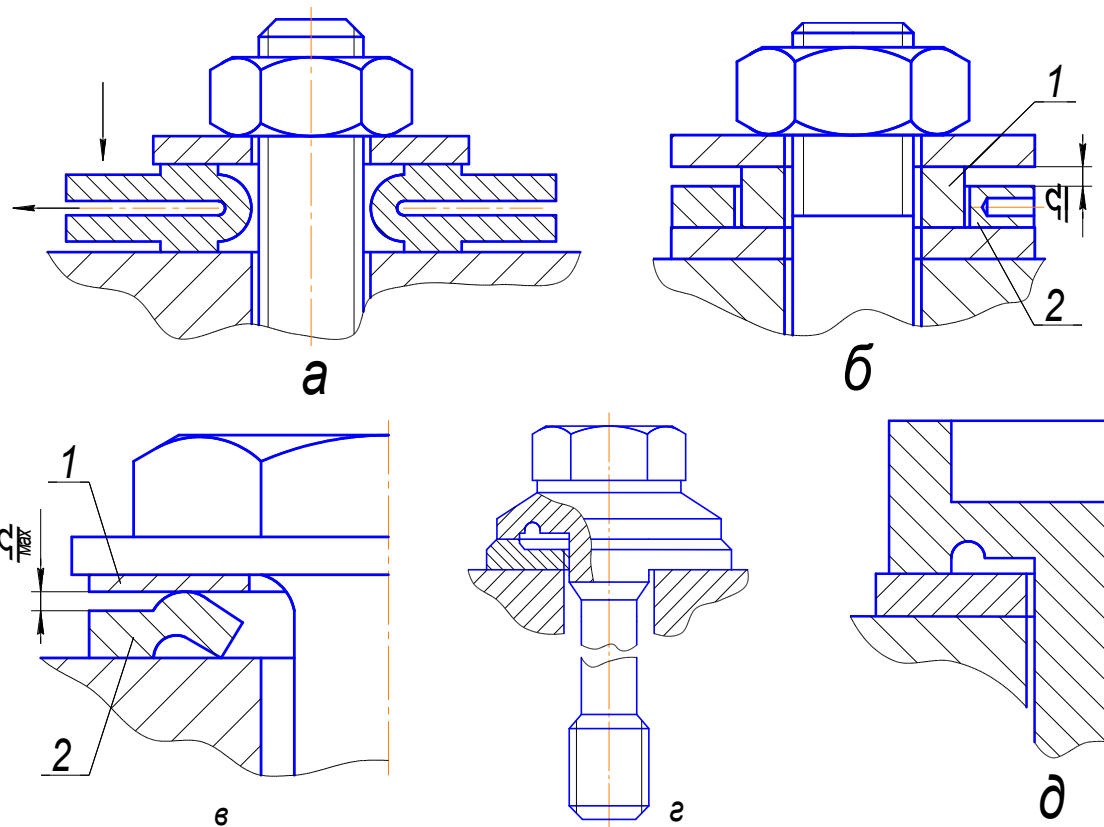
Шайби для контролю сили затягування з'єднань
